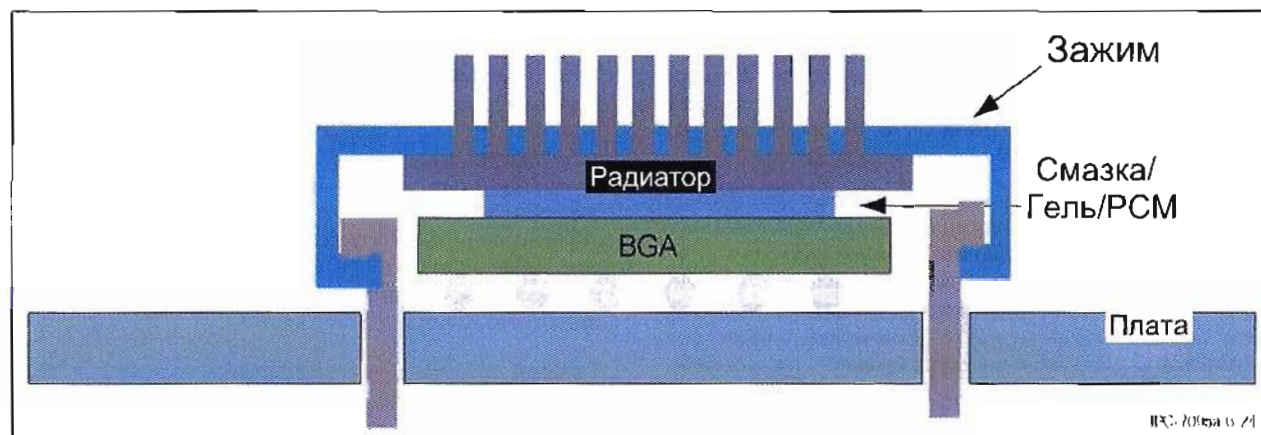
Радиатор, установленный на корпус BGA при помощи зажимов, крепящихся к стойкам, припаянным к печатной плате
